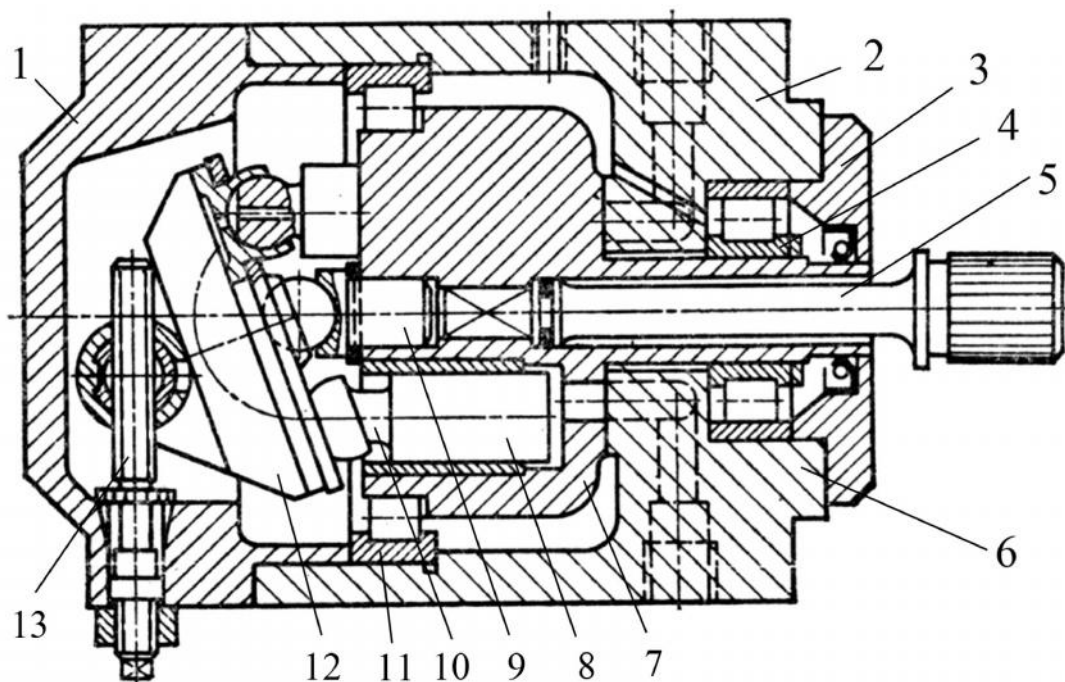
Бескарданный регулируемый насос: 1 – крышка; 2, 6 – корпус; 3 – крышка; 4, 11 – подшипники; 5 – вал; 7 – блок цилиндров; 8 – поршень; 9 – центральный шип; 10 – шатун; 12 – наклонная шайба; 13 – винт регулировочный
